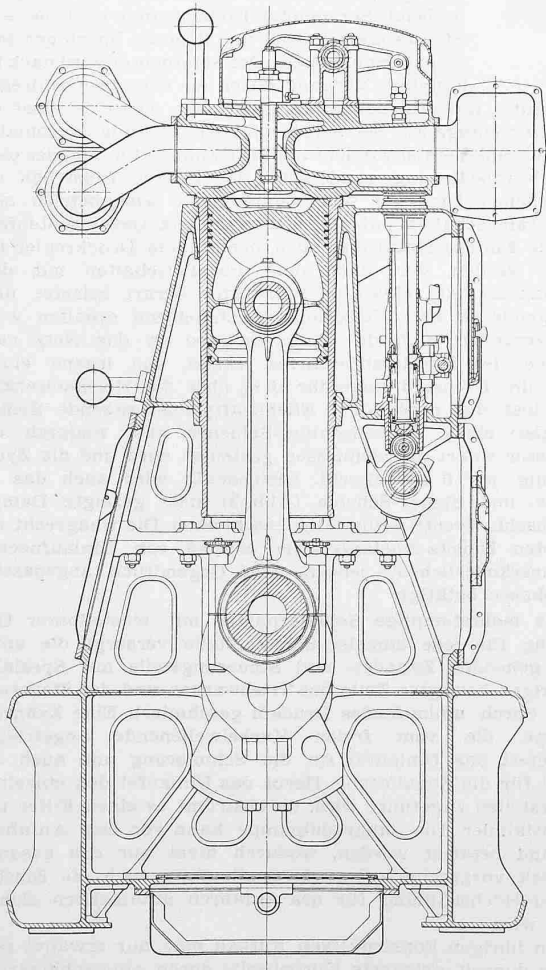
Schnitt durch einen Sulzer-Viertakt-Lokomotivmotor mit Zylinderblock und Kurbelgehäuse in geschweisster Ausführung
